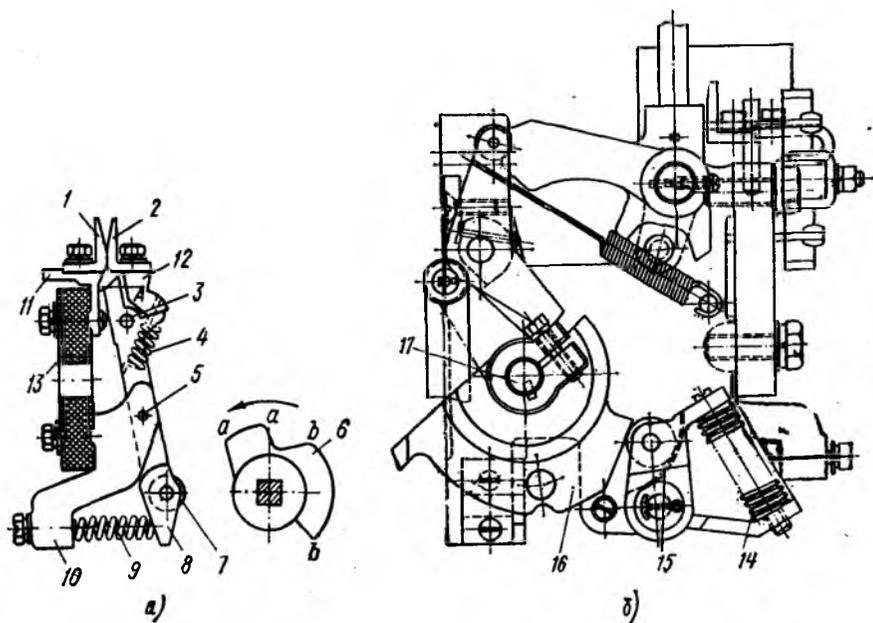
Конструктивная схема контактов контроллера KB-16A (а) и вид контроллера со стороны храпового устройства (б):
